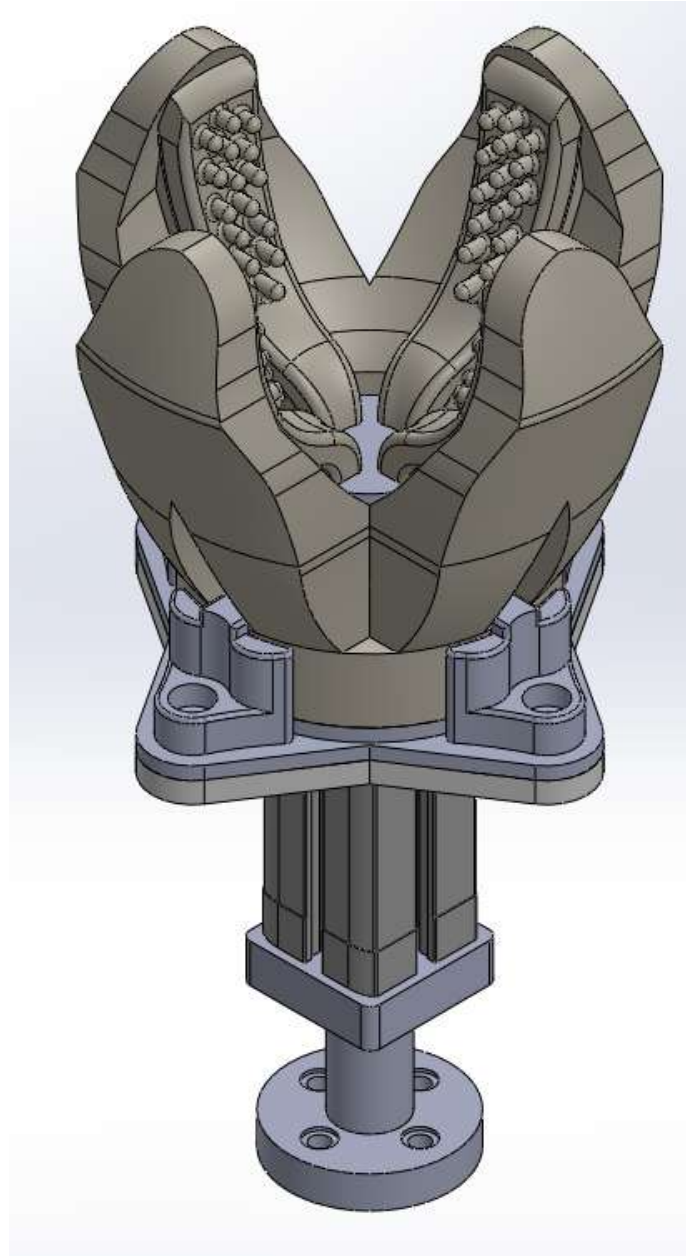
Ensamble final del gripper modelado en SolidWorks.
